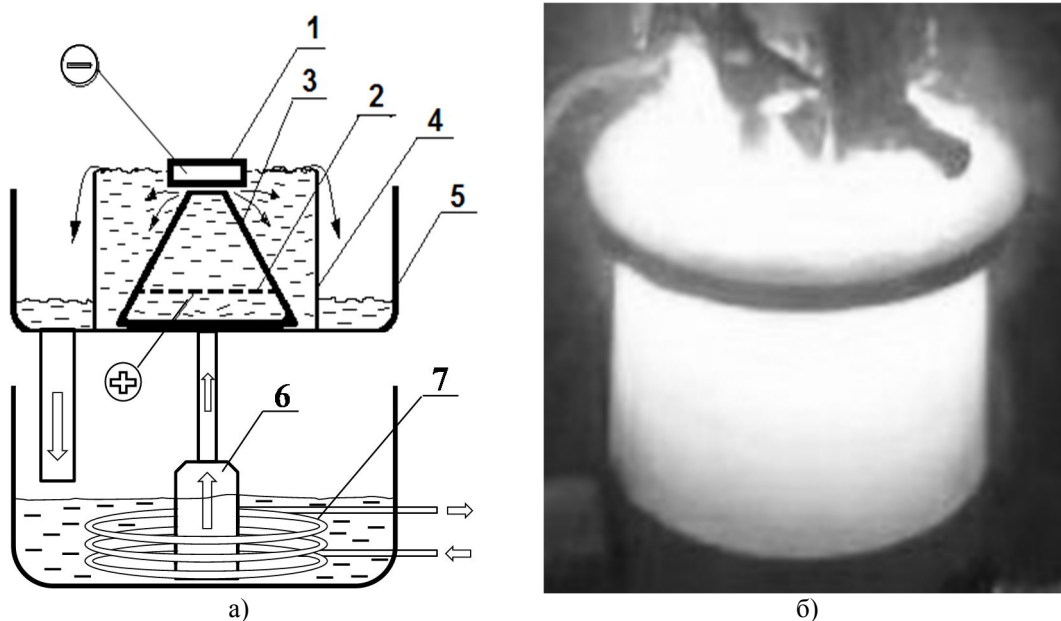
Схема установки и процесс электролитно-плазменного азотирования образца быстрорежущей стали: 1 - обрабатываемый образец (катод); 2 - анод из нержавеющей стали с отверстиями; 3 - конусообразная перегородка; 4 - рабочая камера - ванна с электролитом; 5 - поддон; 6 - насос; 7 - теплообменник
